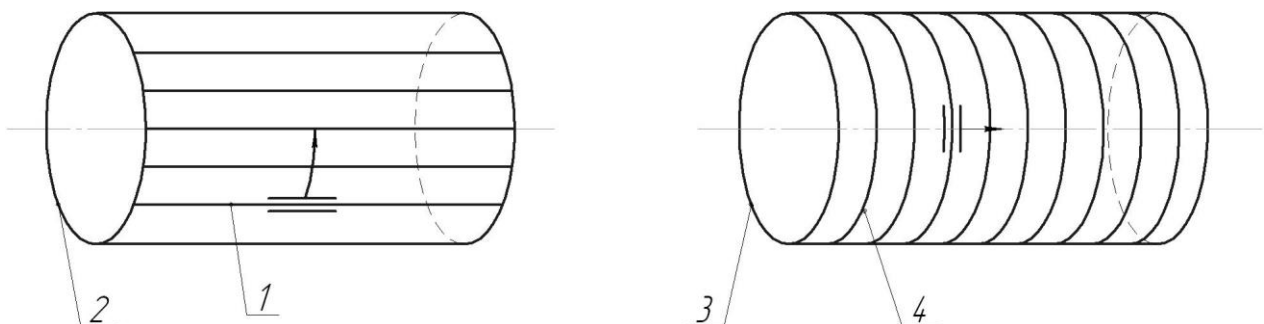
Схема формоутворення циліндричної поверхні
